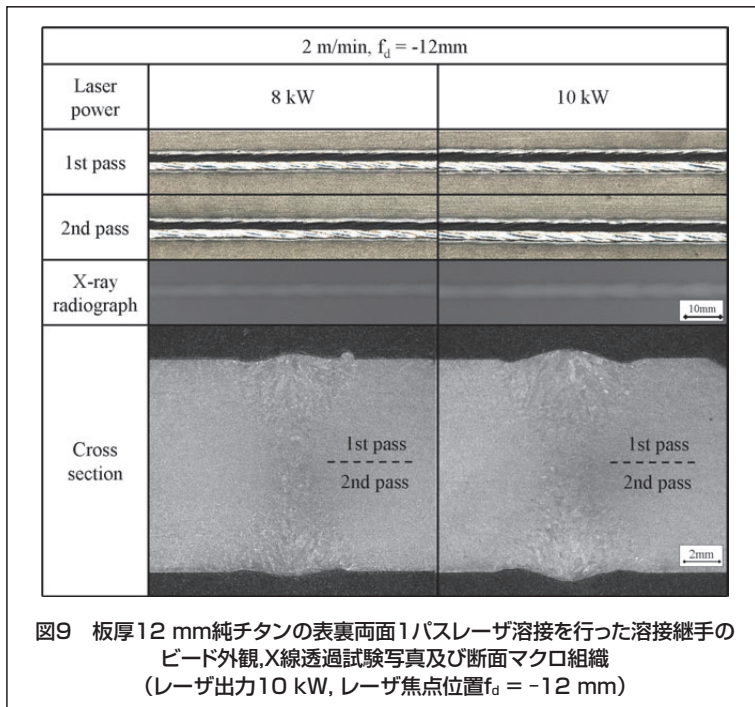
板厚12 mm純チタンの表裏両面1パスレーザー溶接を行った溶接継手のビード外観,X線透過試験写真及び断面マクロ組織 (レーザー出力10 kW, レーザ焦点位置 $f_d = -12$  mm)
